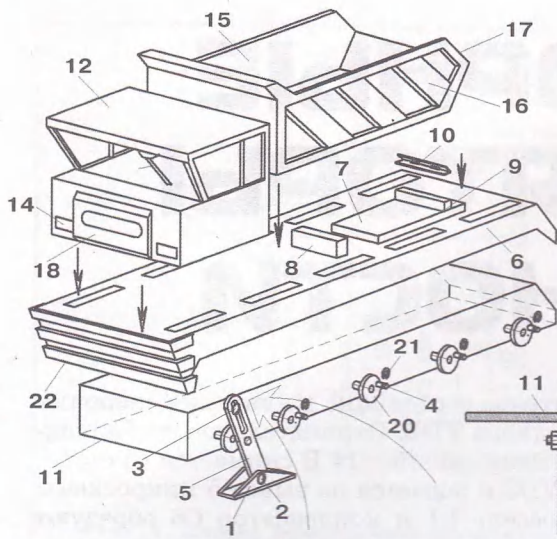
Детали модели: 1 — башмак; 2 — ось; 3 — направляющая ось кулисы; 4 — ось кривошипа-эксцентрика; 5 — кулиса; 6 — платформа; 7 — короб гидроприемника; 8 — опора кузова; 9 — упор; 10 — петля; 11 — рама; 12 — кабина; 13 — стеклоочиститель; 14 — фара; 15 — кузов; 16 — ребро жесткости; 17 — борт кузова; 18 — решетка радиатора; 19 — втулка; 20 — эксцентрик; 21 — стопорное кольцо; 22 — полоски платформы.
